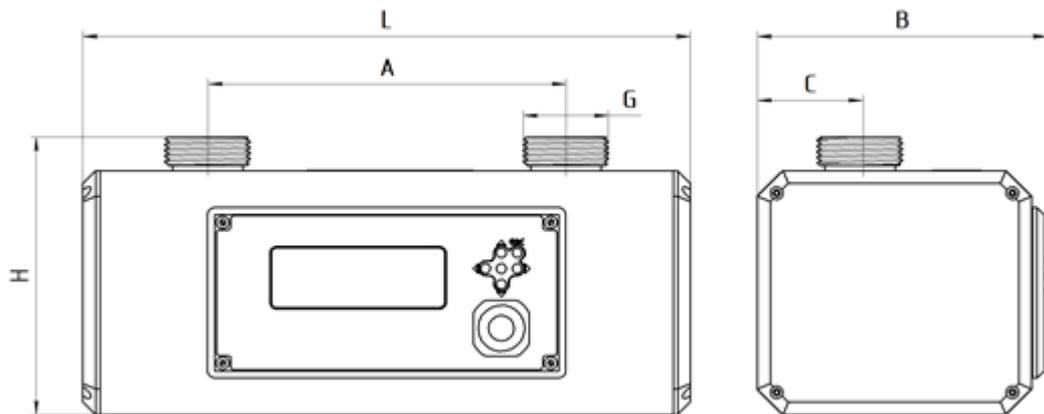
Габаритно-присоединительные размеры комплексов исполнения V, VP с вертикальным расположением патрубков (см. таблицу 7)
